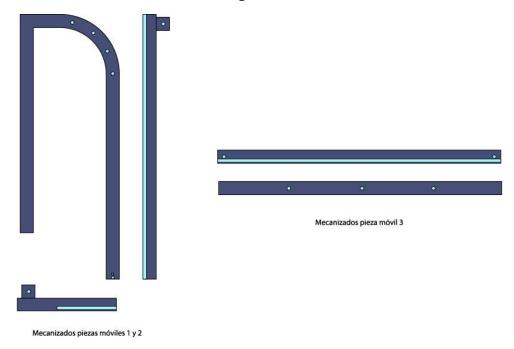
Croquis proceso de mecanizado perfiles conjunto móvil
